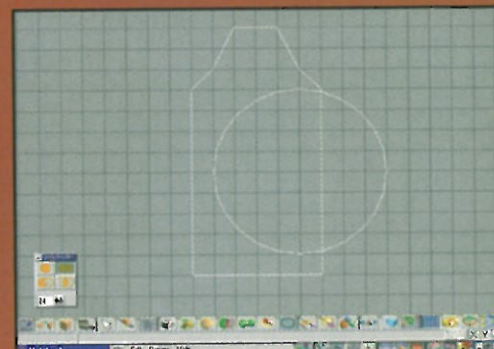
EL SHAPE CIRCULAR SE PONE EN ESTA POSICIÓN PARA REALIZAR LA BOOLEANA Y EL SHAPE DEL CHASIS.
